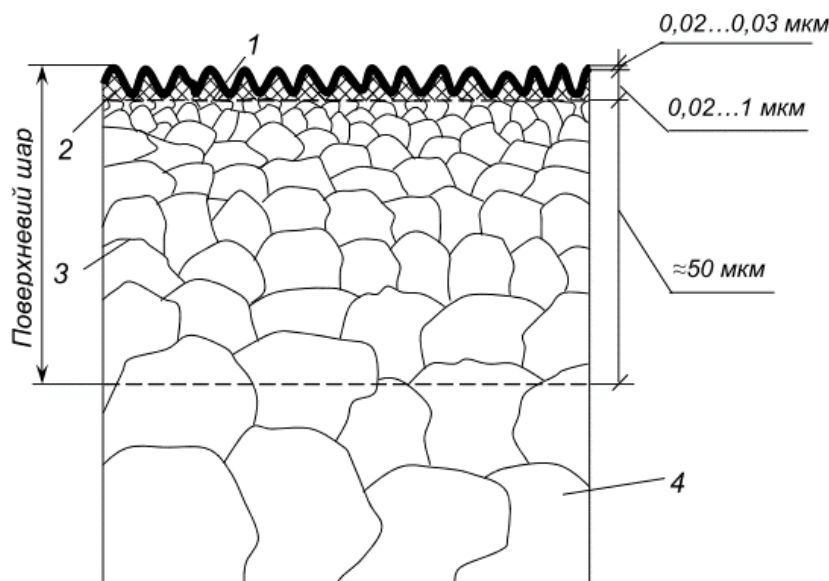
Структура поверхнього шару шліфованої сталеві деталі
